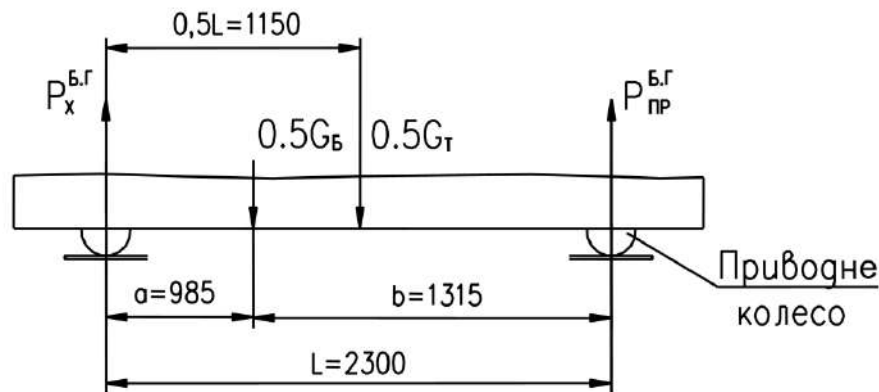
Схема навантажень на кінцеву балку візка при пересуванні без вантажу.
